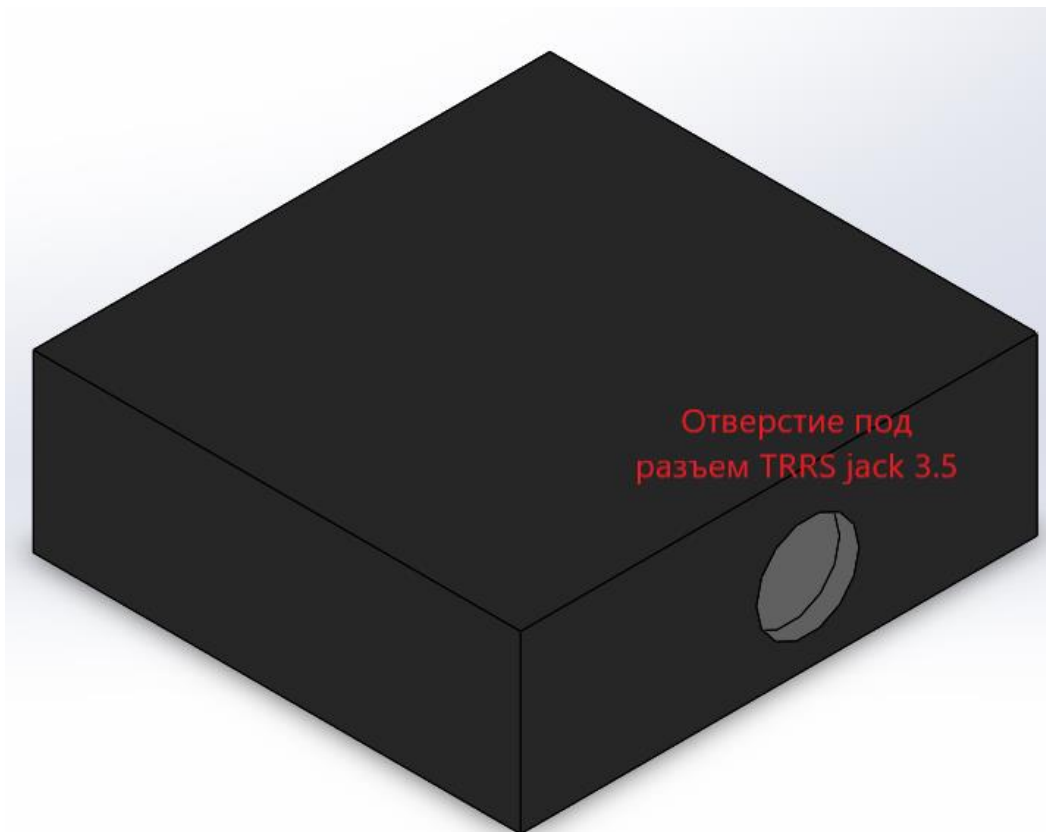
Внешний вид корпуса со стороны разъема TRRS jack
